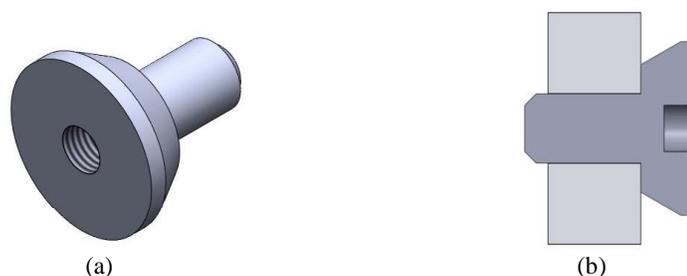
(a) Pino universal e (b) Vista em corte do conjunto furo pino montado
